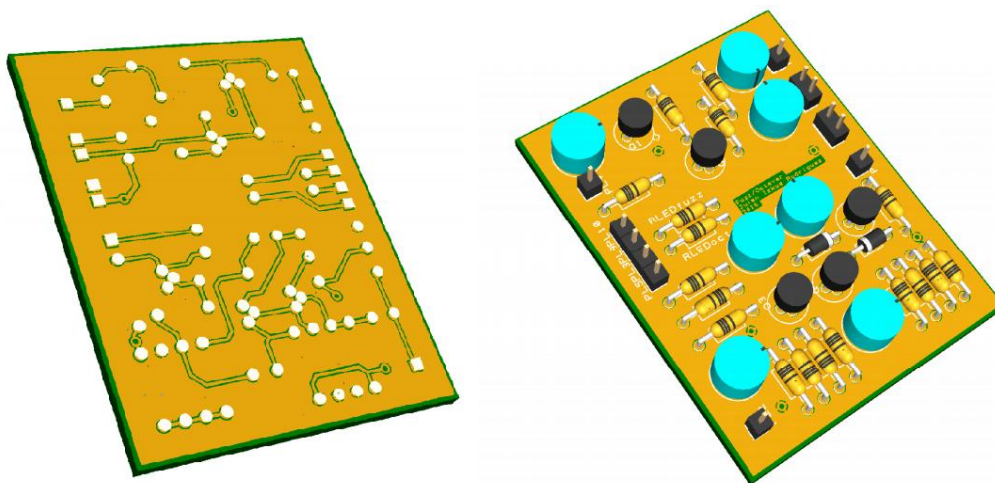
VISTA 3D DEL PCB DISEÑADO EN DESIGNSPARK
